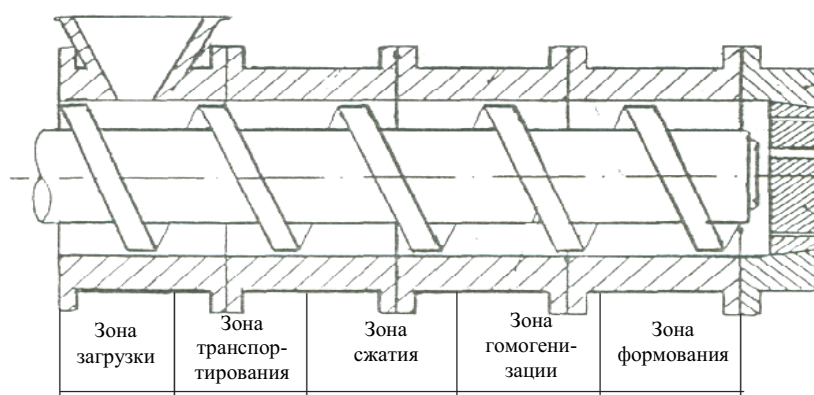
Рабочий узел шнековой камеры пресс-экструдера
